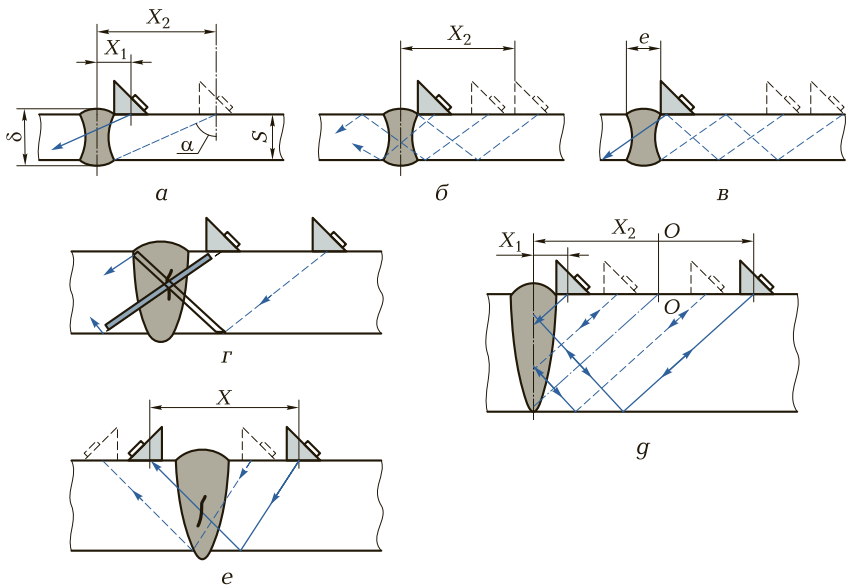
Схемы «прозвучивания» стыковых сварных швов:
